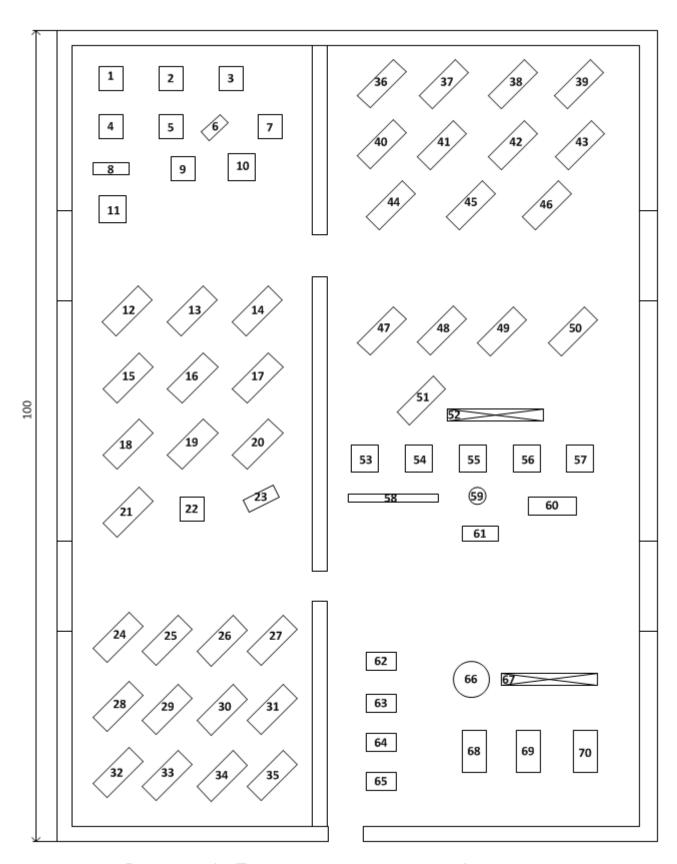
Генплан цеха по ремонту оборудования
